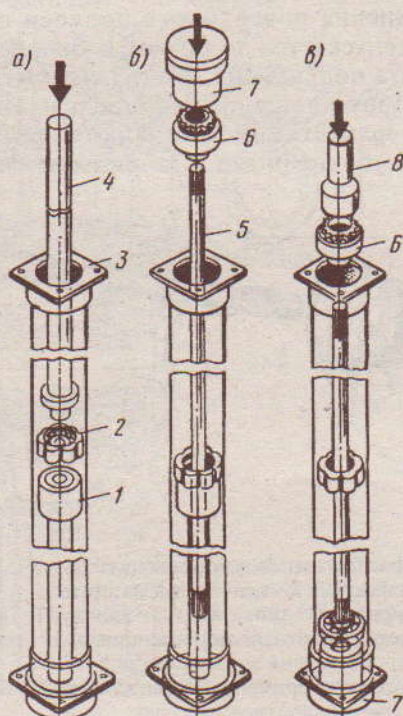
Сборка приводного вала: а - запрессовка в кожух подушки со средним подшипником в сборе; б - запрессовка вала в средний подшипник и зубчатого хвостовика с подшипником в сборе в кожух; в - запрессовка второго зубчатого хвостовика с подшипником в сборе в кожух; 1 - подставка (см. рис. 128); 2 - средний подшипник с подушкой в сборе; 3 - кожух приводного вала; 4 - оправка; 5 - приводной вал; 6 - зубчатый хвостовик с подшипником в сборе; 7 - оправка; 8 - оправка
